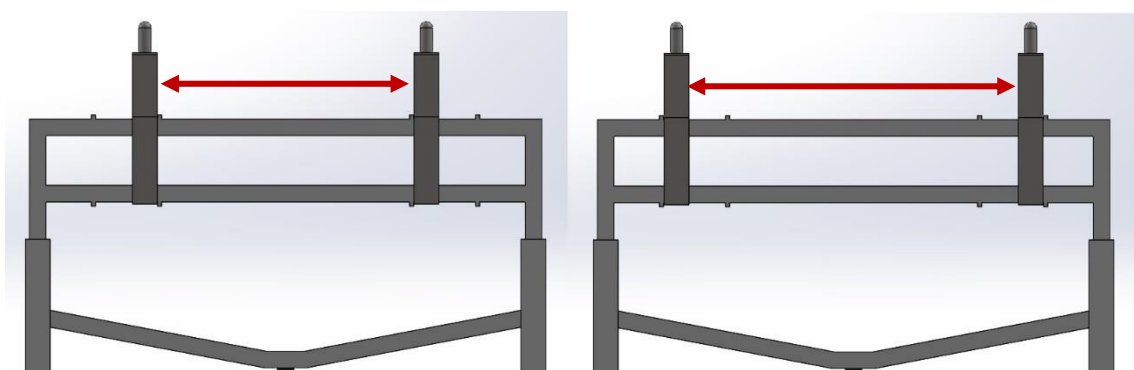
Detalhe dos elementos móveis para adaptação do apoio a cabines estreitas e largas
